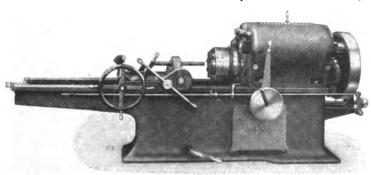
Gewindeschneidmaschine für Kuppel- und Bremsspindeln von Gustav Wagner, Reutlingen.
